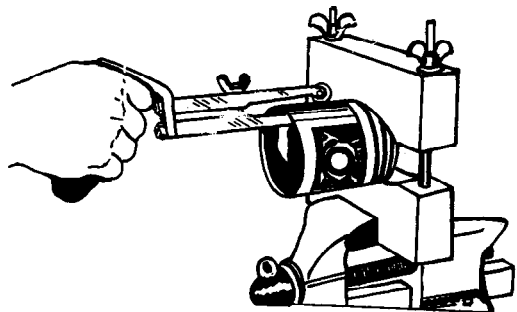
Reacondicionador de las dimensiones del pistón. La presión ejercida entre ambas ruedecillas comprime el metal y ensancha la falda (*Sealed Power Corporation*).
